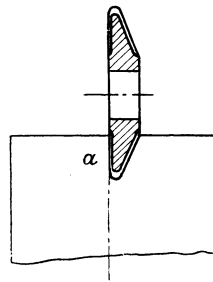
Das Fräsen der Nuten für hinterdrehte Stirnzähne.
